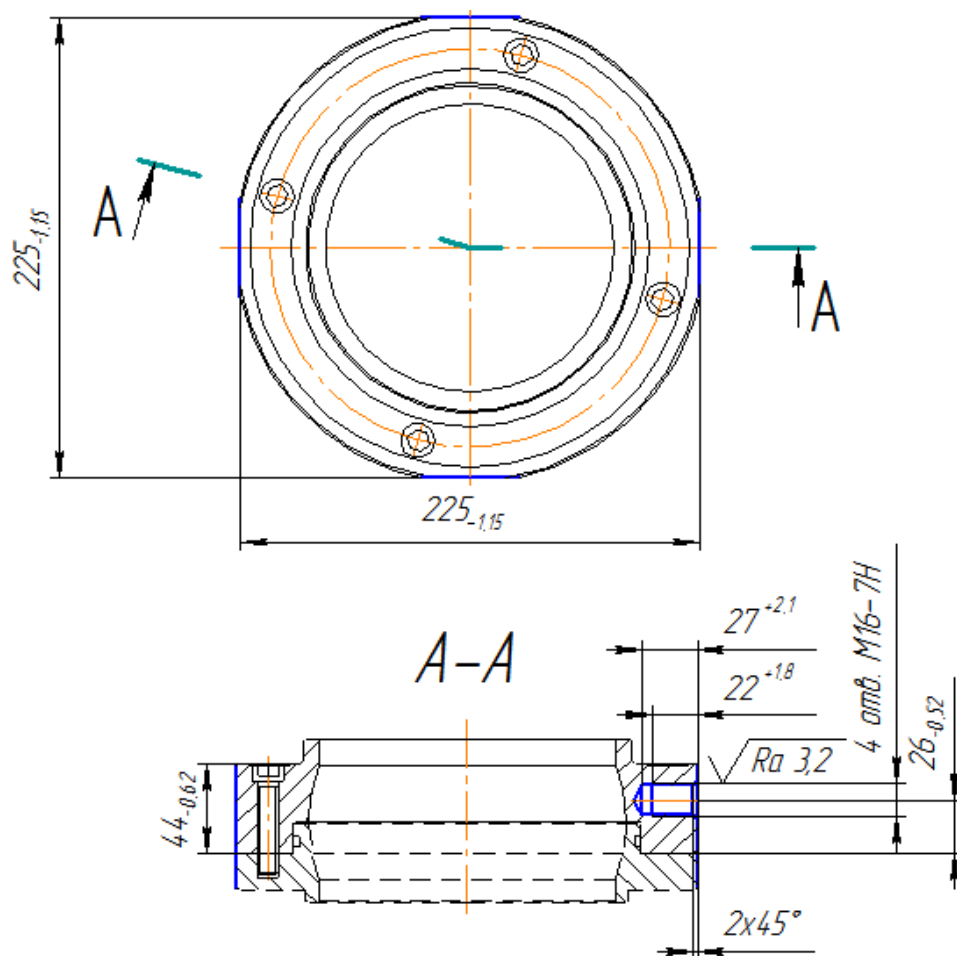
Ескіз обробки заготовки на операції 035
